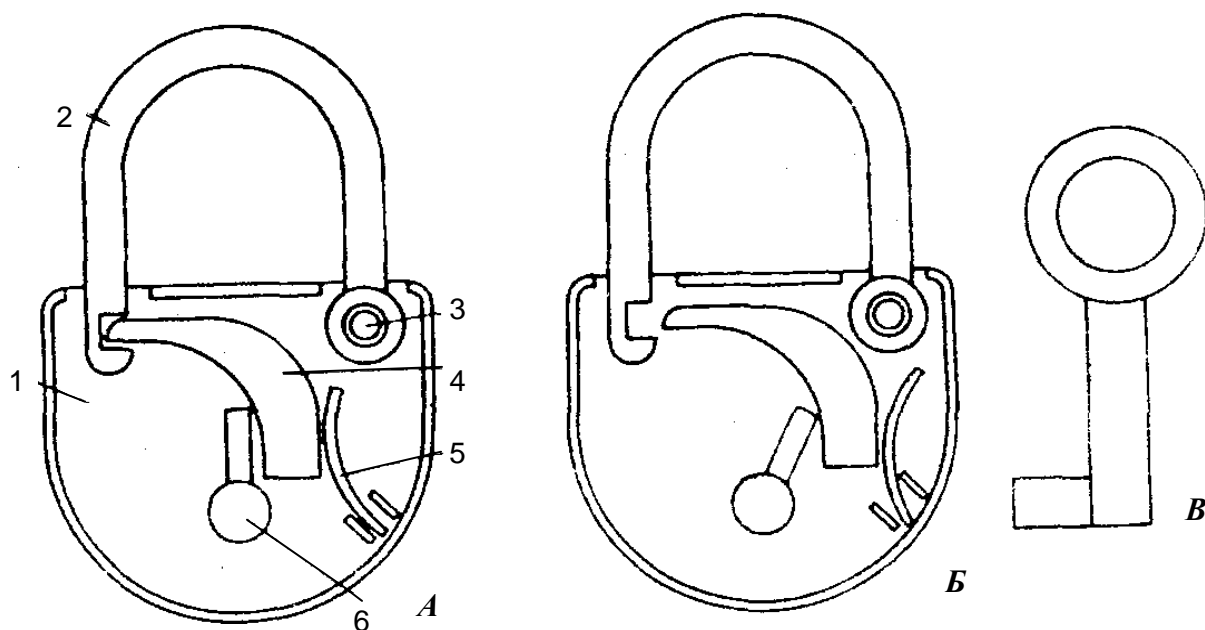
Устройство навесного замка с пружинным механизмом:
